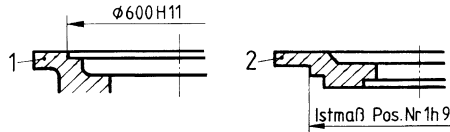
Anpassen mit vorgeschriebener Passtoleranz an zuerst gefertigtes Gegenstück (Teil 1)
